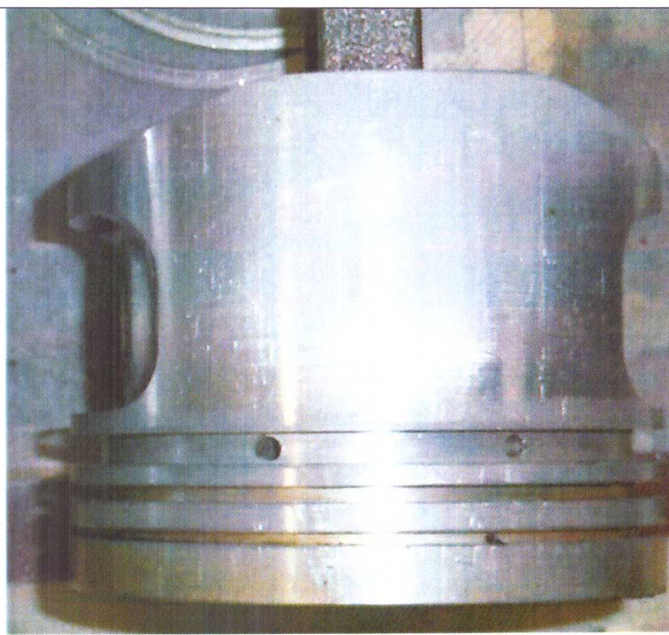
Внешний вид боковой поверхности поршня второго цилиндра по окончании длительных испытаний двигателя при работе на базовом масле Castrol EDGE с добавкой нанокompозита Amortect PROOF
